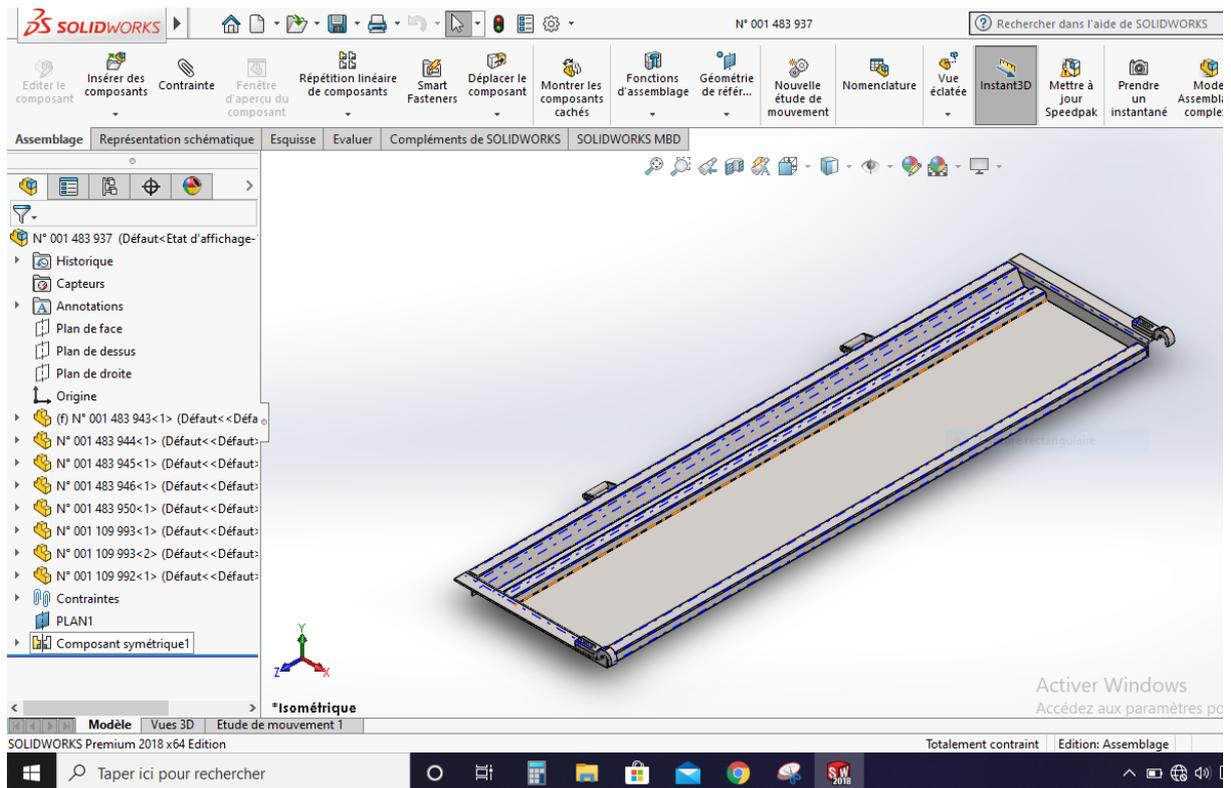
porte arrière de benne de camion k120 c088 en solidworks
